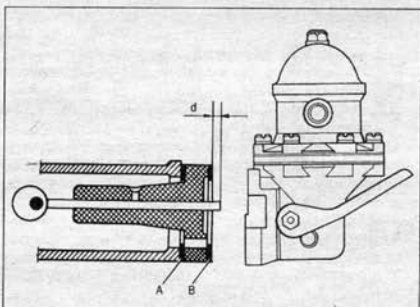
Схема контроля и регулировки выступа толкателя привода насоса:
